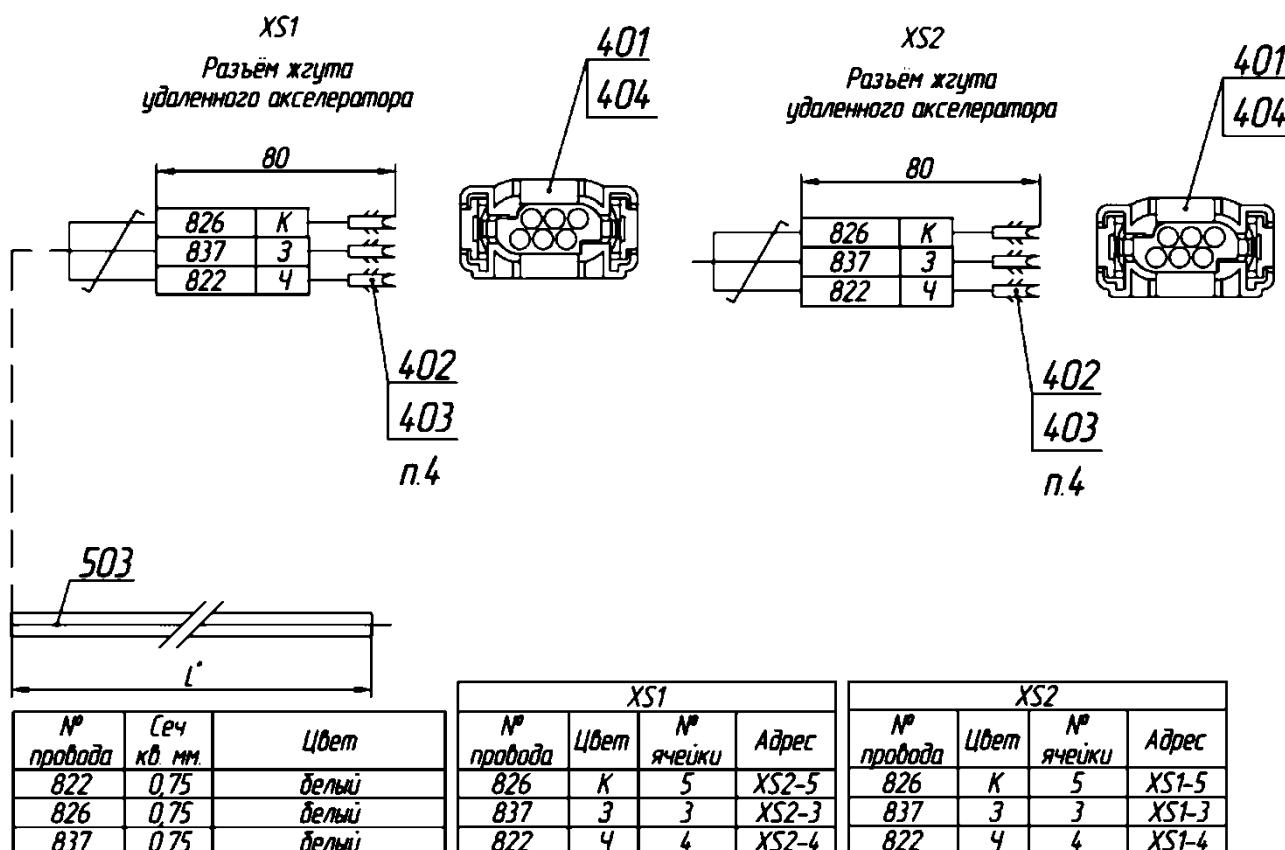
Жгут дополнительный педали управления подачей топлива:
